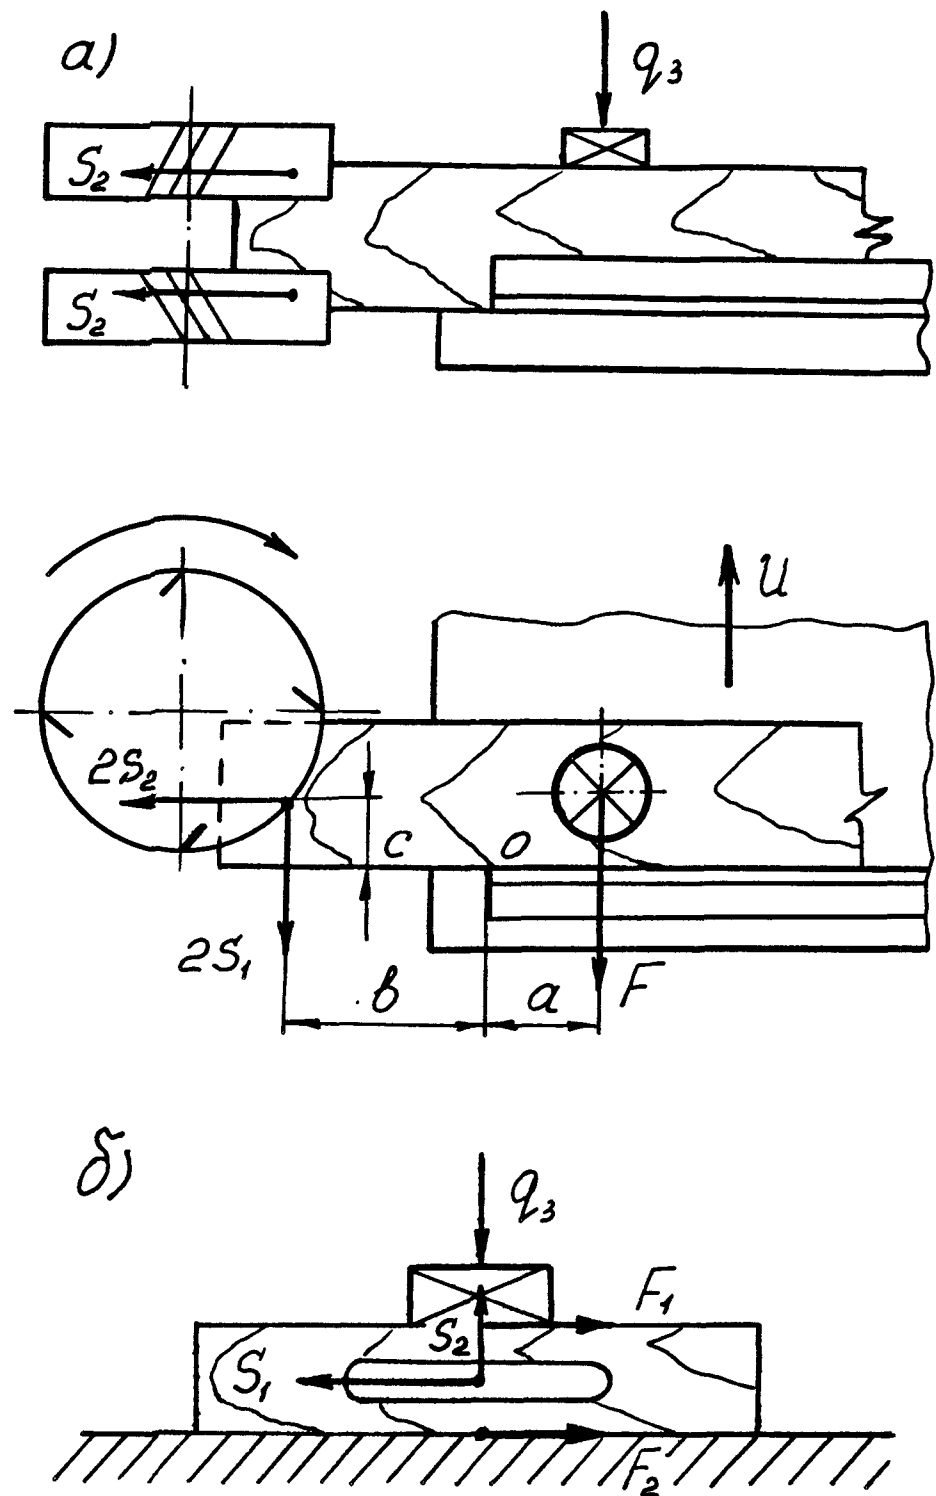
Расчетные схемы для определения давления зажимного устройства: а - станок с подачей заготовки кареткой; б - станок с подачей заготовки столом
